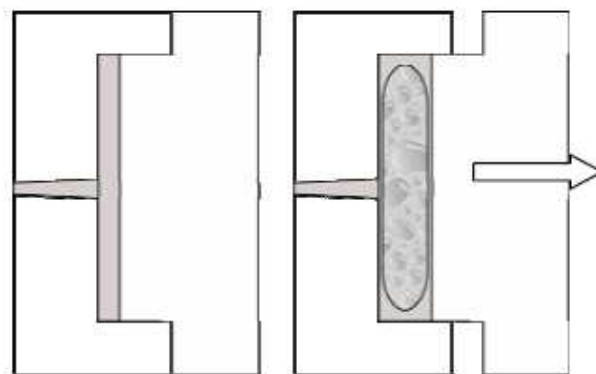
Moldagem de injeção com expansores químicos a alta-pressão [20].
